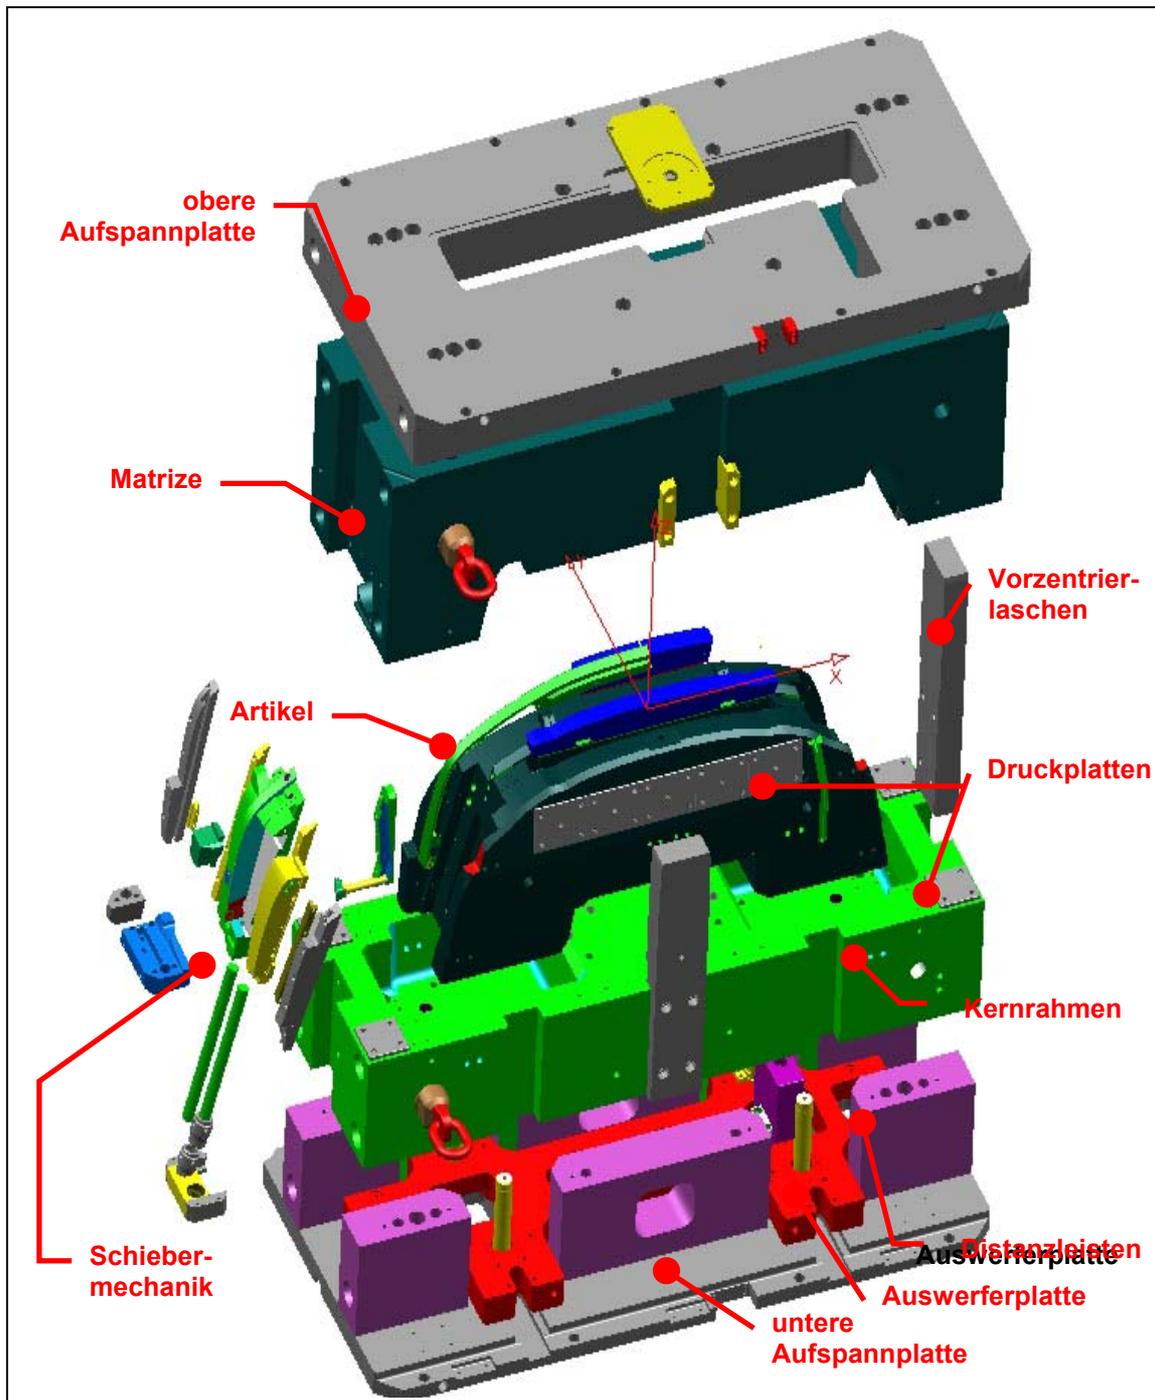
Komplettes Werkzeug nach Abschluss der Konstruktion
